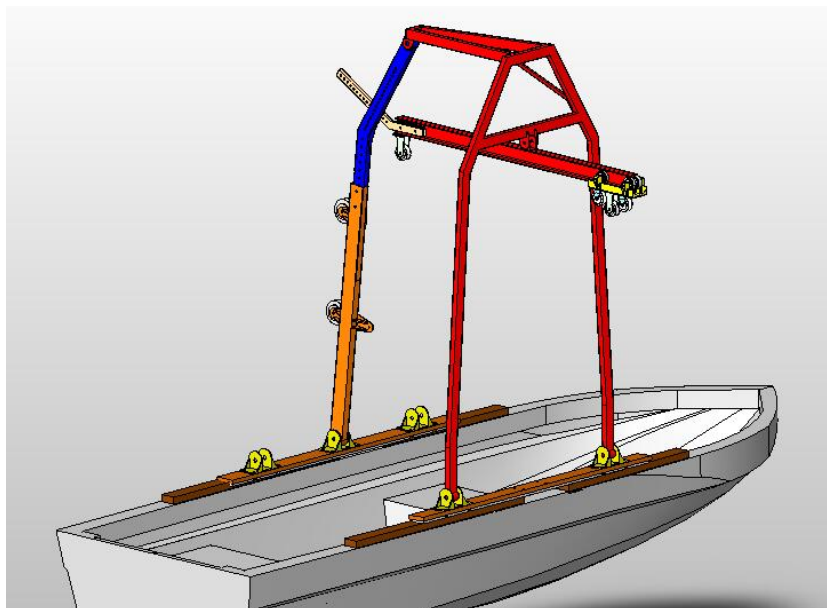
Configuração inicial da estrutura com 3 pontos de apoio e viga I
